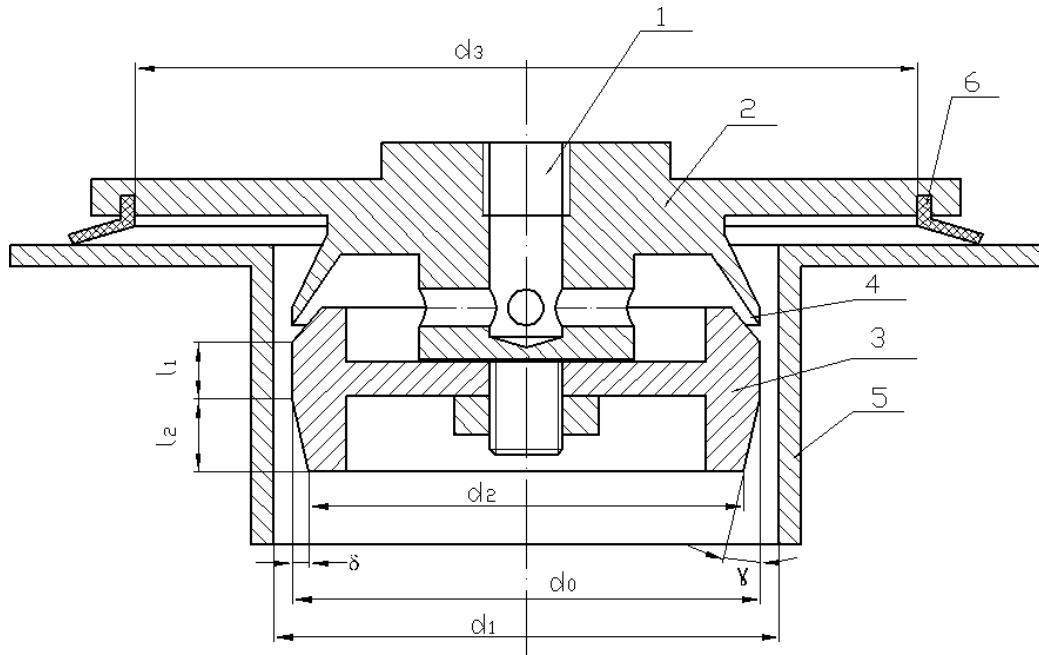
Конструктивна схема струменевого захоплювача для об'єктів з наскрізними циліндричними отворами
